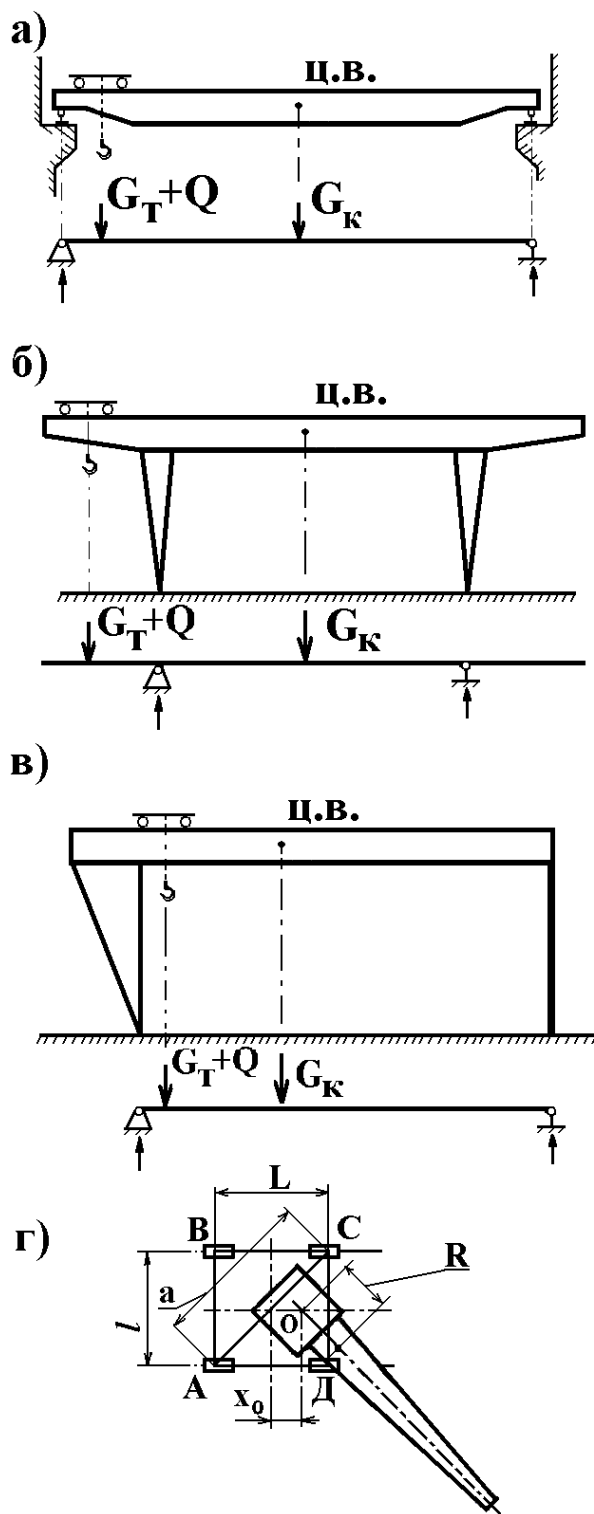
Схеми навантажень на ходові колеса кранів
